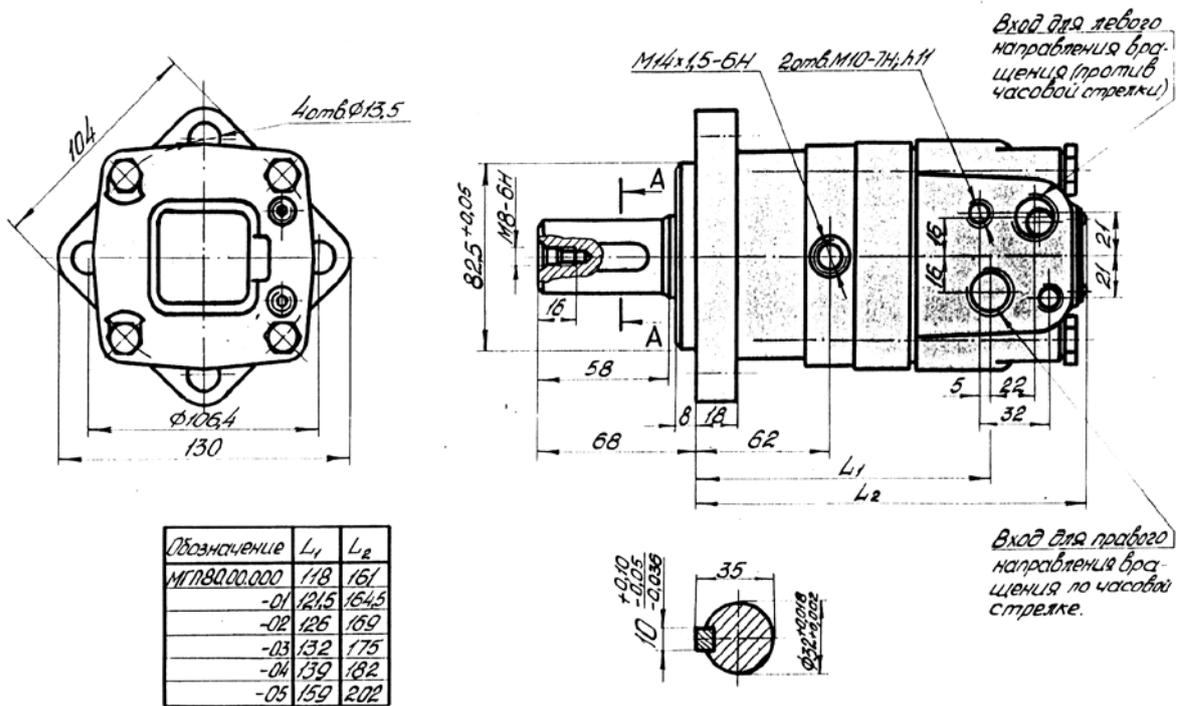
Гидромотор планетарный типа МГП (габаритные размеры)
